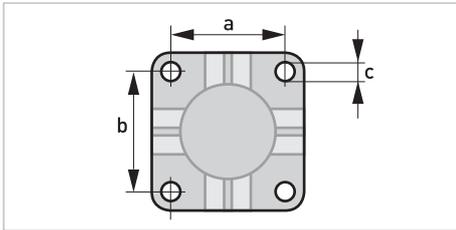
Abmessungen der Montageplatte für das Feldgehäuse
